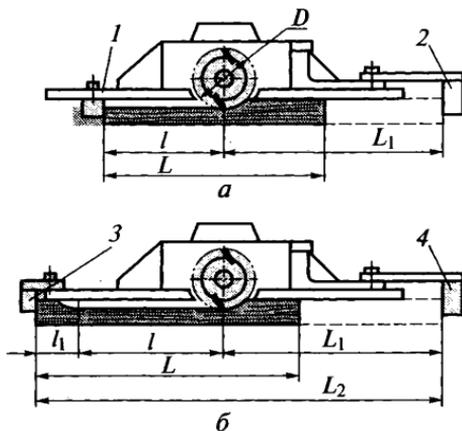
Настройка ограничительных упоров фрезерного станка:
